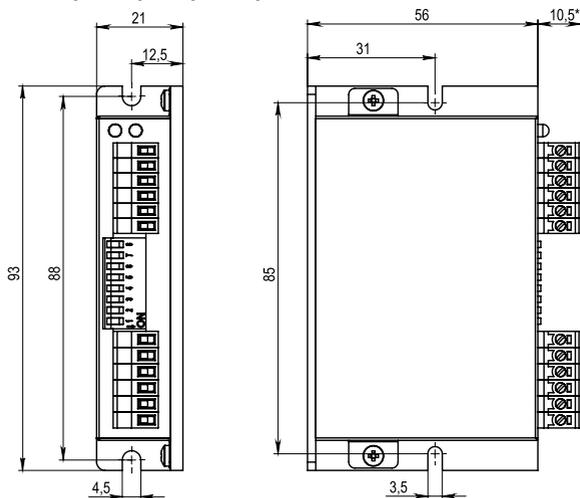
габаритные размеры драйверов SMD-20.17.16.R2
